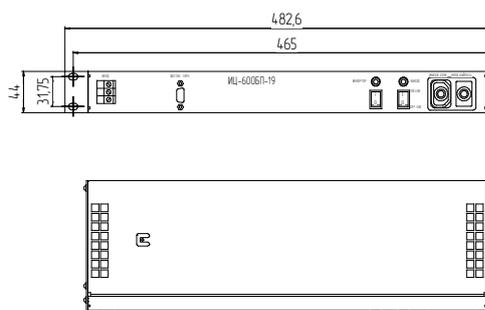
Габаритный чертеж ИЦ-600 БП-19
